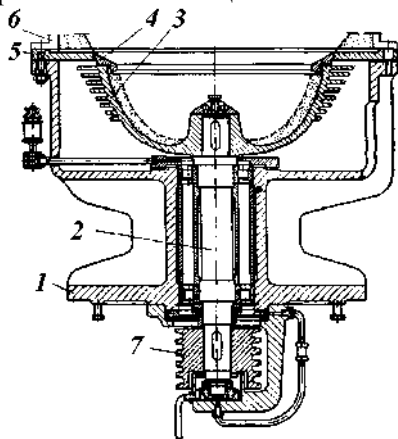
Центробежная мельница самоизмельчения: 1 – корпус; 2 – приводной вал; 3 – чаша; 4 – защитное кольцо; 5 – размольное кольцо; 6 – сепаратор; 7 – шкив.
